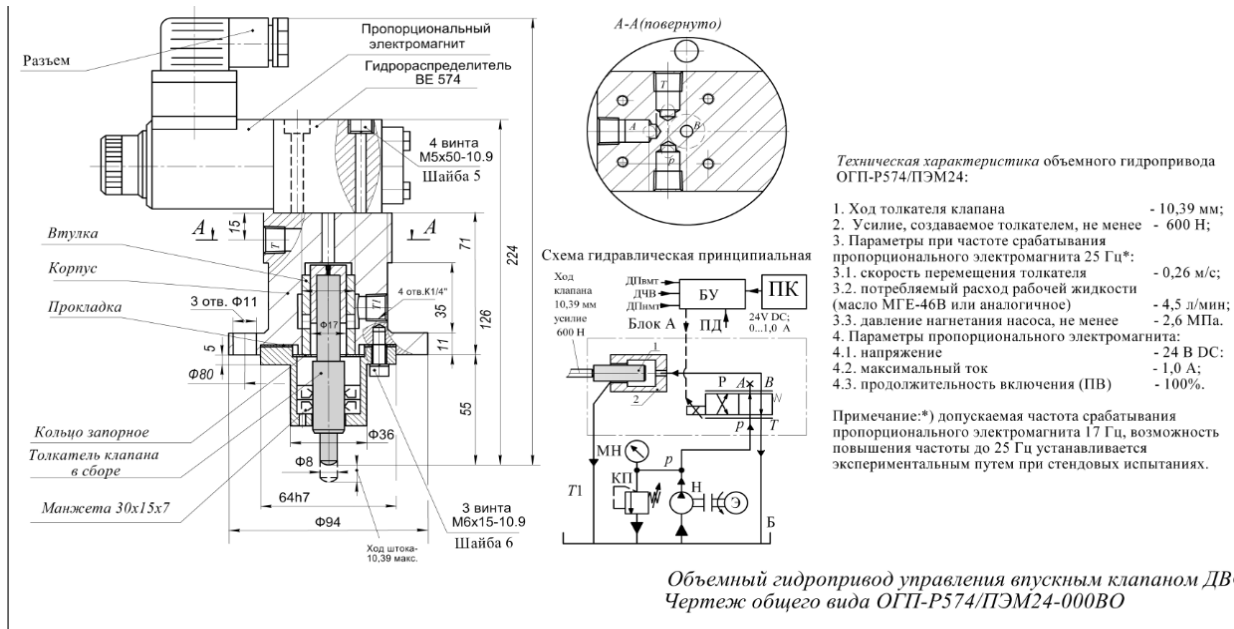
Загальний вид об’ємного гідроприводу для керування впускним клапаном пневмодвигуна на базі ДВЗ
